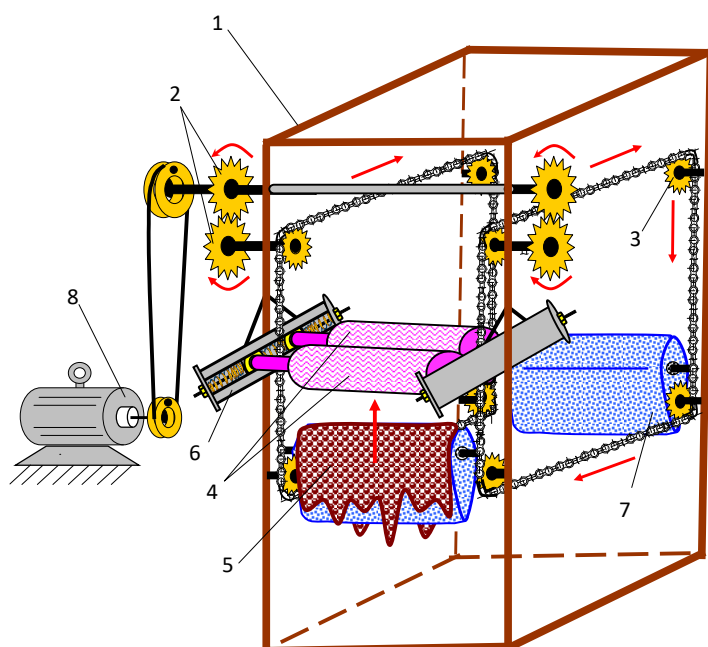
Схема предлагаемой валковой машины: 1-станина, 2-зубчатые колеса, 3-звездочки, 4-отжимные валы, 5-кожевенный полуфабрикат, 6-механизм давления, 7-опорная плита, 8-электродвигатель
